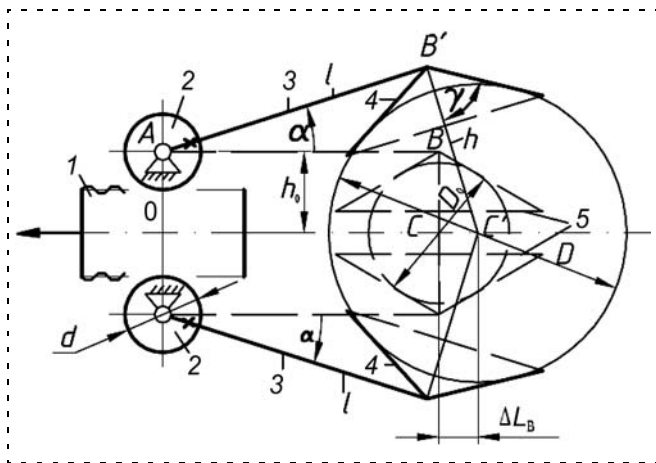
Преобразователь движения мехатронного модуля захватного устройства с подвижной рейкой
